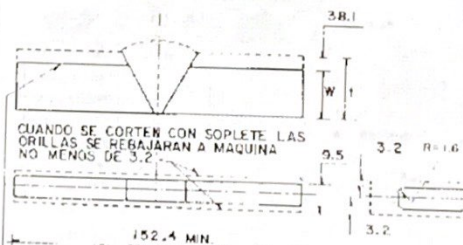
ESPECIMENES PARA PRUEBA DE DOBLADO EN LA CARA Y EN LA BASE
